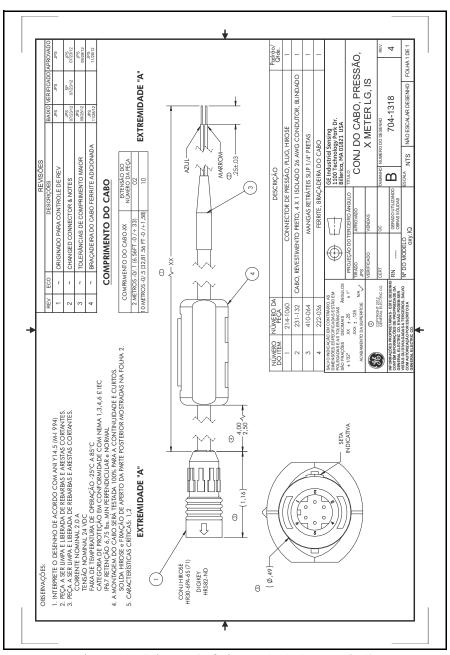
Cabo, IS (ref. des. 704-1318, FL 1 de 2)
